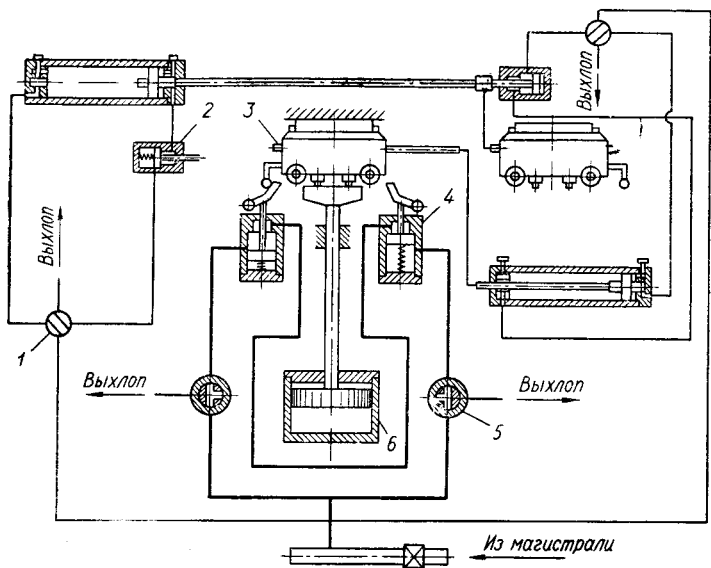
Пневматическая схема прессовой машины ПФ-4
